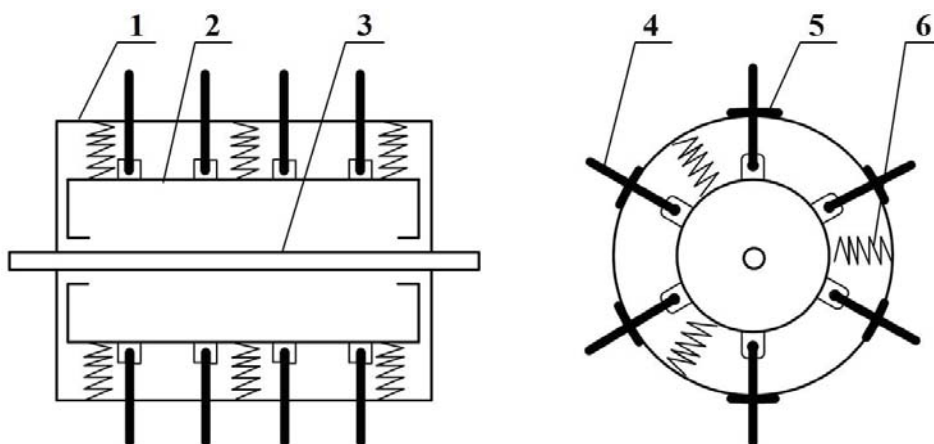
Схема конструкции катка ударного действия: 1 - наружный барабан; 2 - внутренний барабан; 3 - ось; 4 – шпора; 5 – защитный кожух; 6 – пружина
